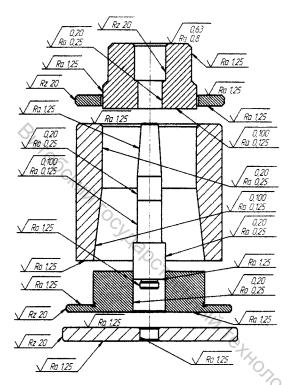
Параметры шероховатости поверхностей основных деталей пресс-форм:
